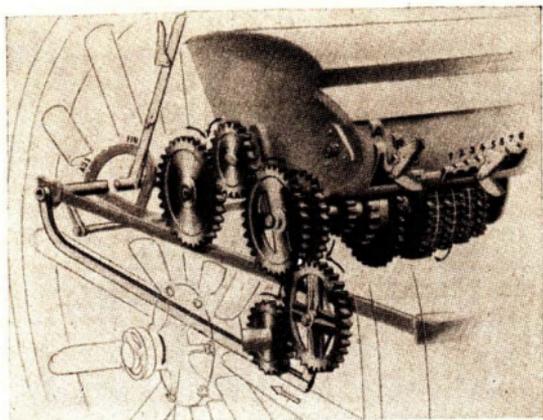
/1. Vielstufengetriebe einer Drillmaschine
